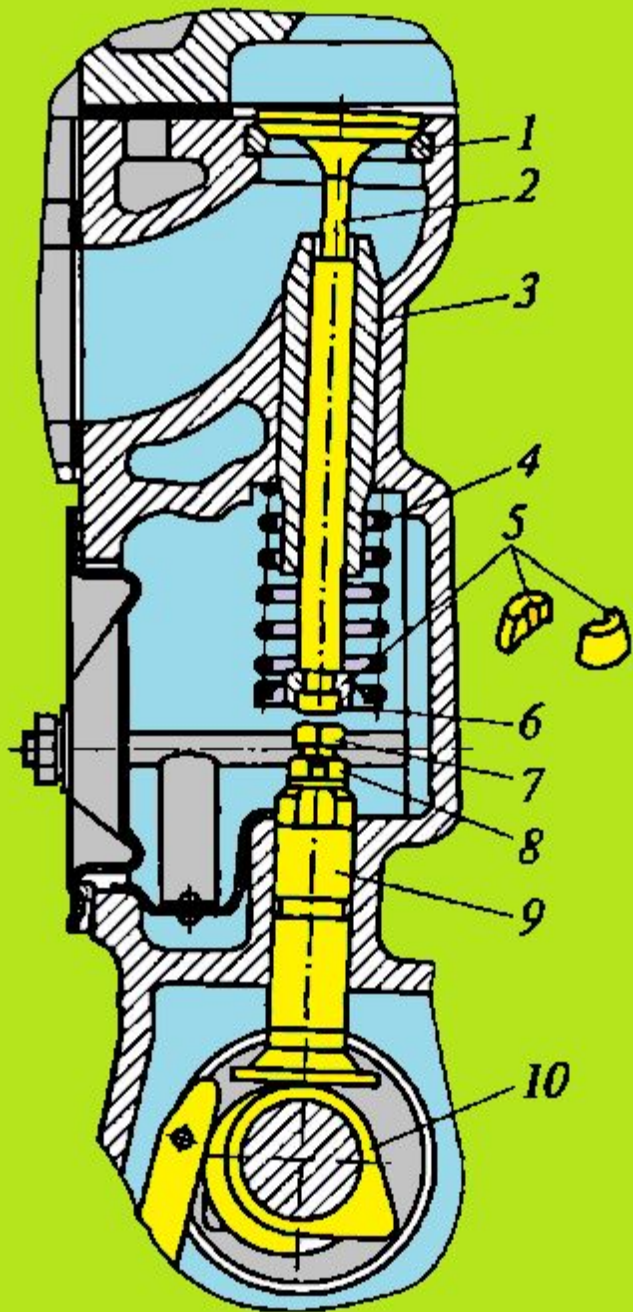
а. Газораспределительный механизм с нижним расположением клапанов и распределительного вала;
